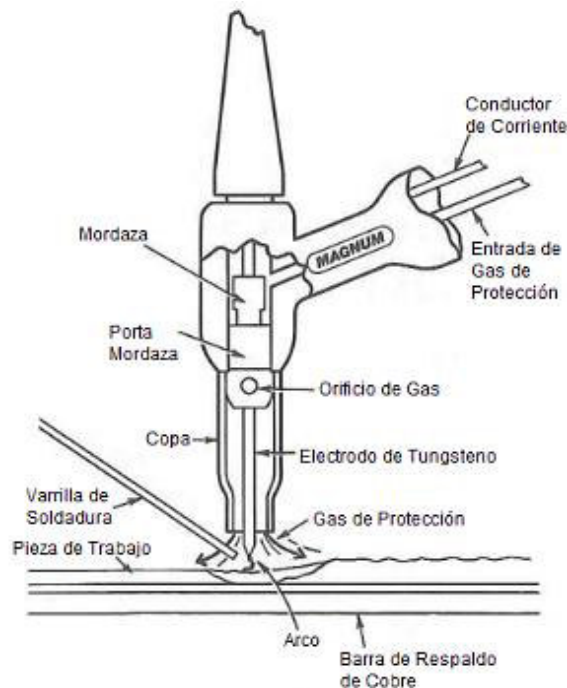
Soldadura por arco con electrodo de Tungsteno bajo protección gaseosa.
